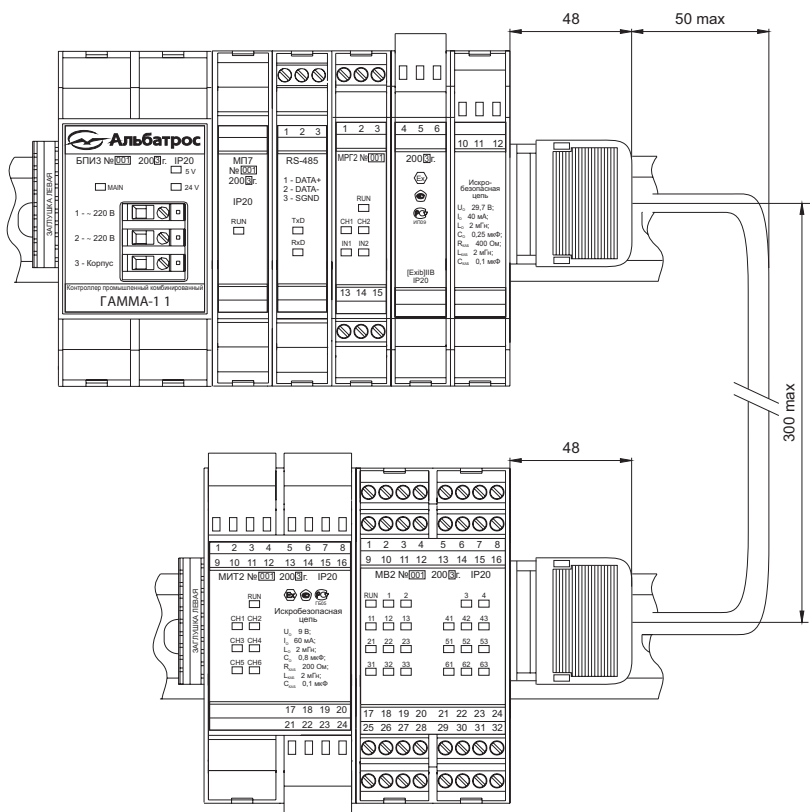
Внешний вид и габаритные размеры составных частей прибора (вариант установки на два DIN-рельса)
